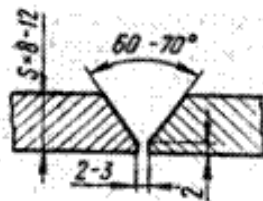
Подготовка кромок труб под сварку при толщине стенок 8—12 мм
